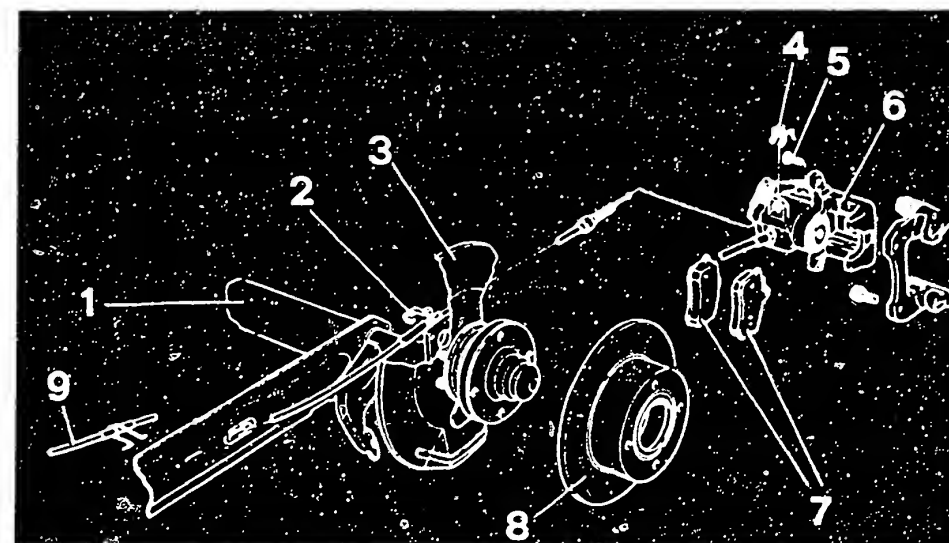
Scheibenbremsen hinten: 1 Hinterachse - 2 Distanzhalter - 3 Abdeckblech - 4 Federklammer - 5 Schraube - 6 Bremssattelgehäuse - 7 Bremsklötze - 8 Bremsscheibe - 9 Handbremsseile.
